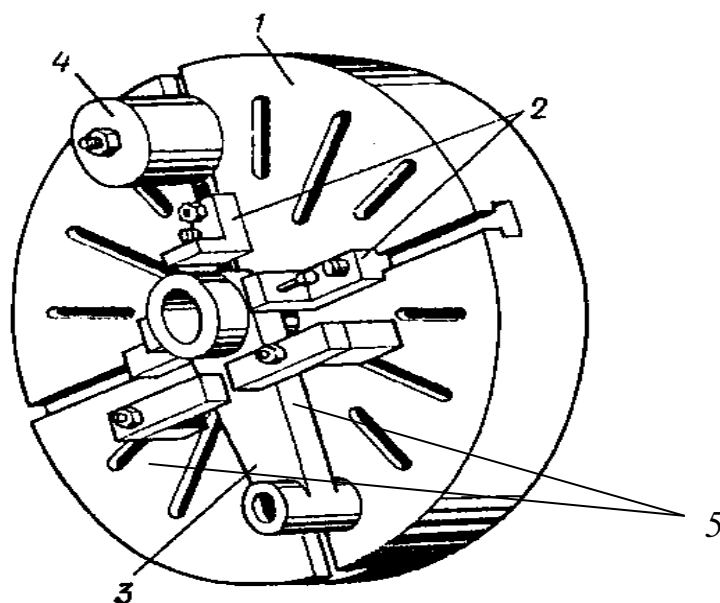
Планшайба с закреплённой заготовкой: 1 – планшайба; 2 – угольники зажимные с винтами; 3 – заготовка (кронштейн); 4 – противовес; 5 – прихваты
